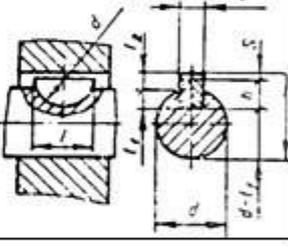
Шпонкове з'єднання: а – загальний вигляд; б – деталі
